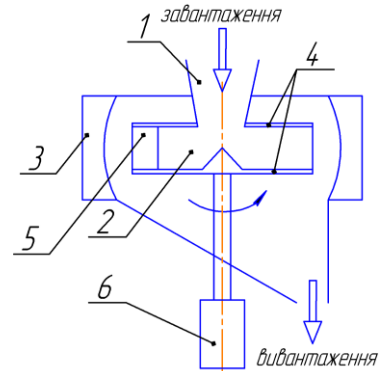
Принципова схема ударно-відцентрової дробарки з вертикальним валом робочого органу
